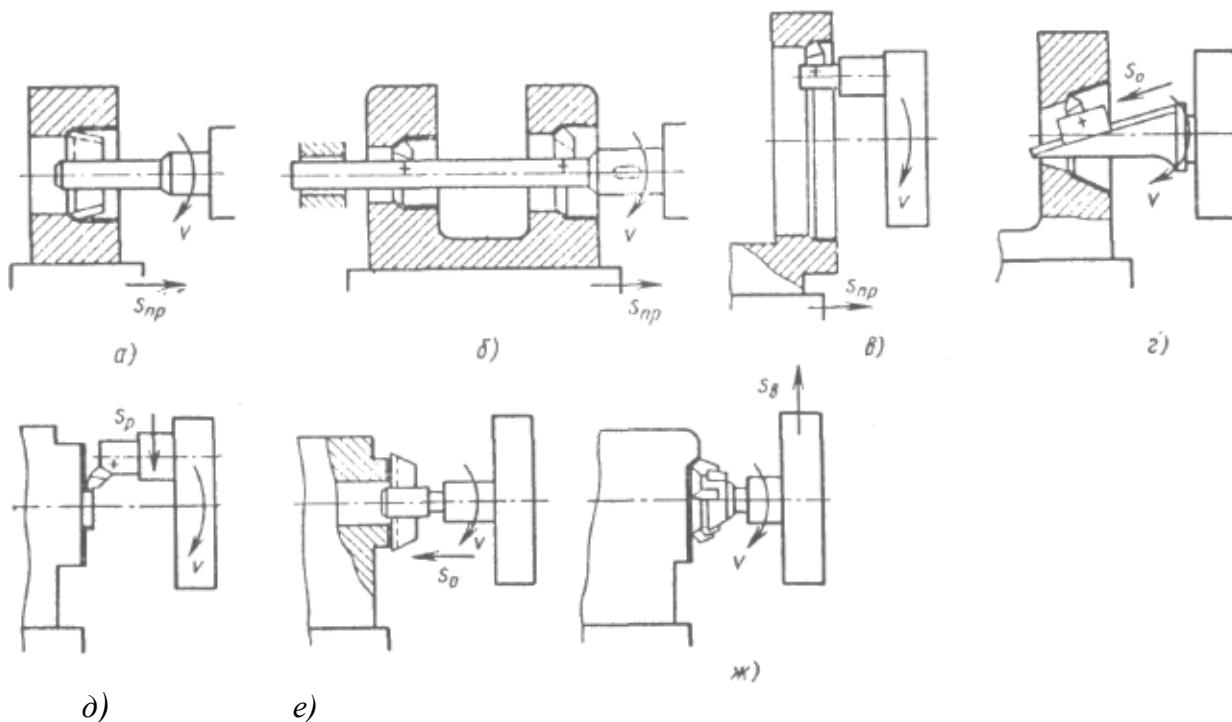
Схемы обработки заготовок на горизонтально-расточных станках: а – двухлезвийным пластинчатым резцом; б – одновременно 2-х соосных отверстий; в, г, д – резцом, закрепленным на суппорте планшайбы; е – цекование торца; ж – фрезерование торца
